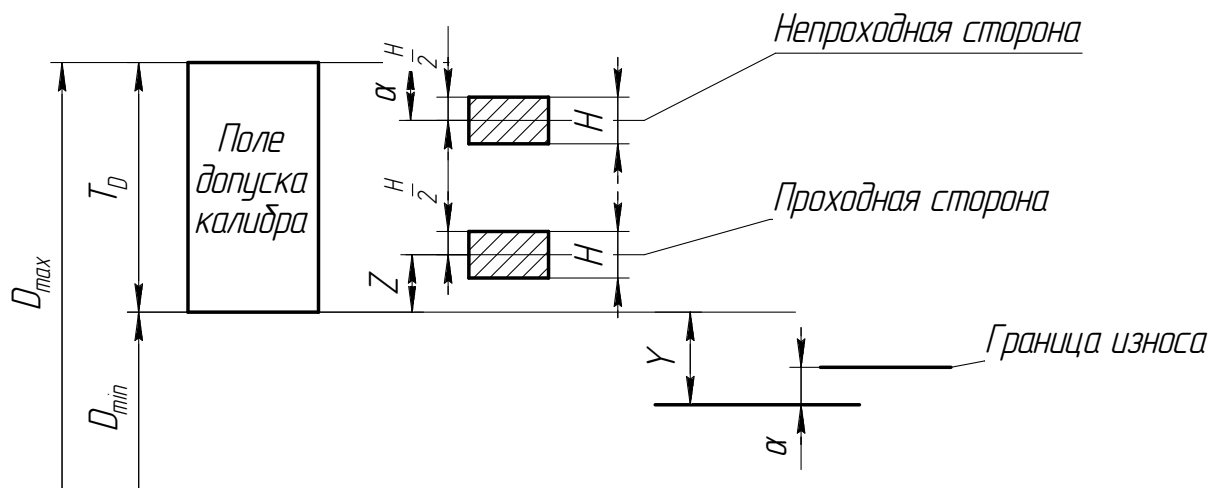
Схема расположения полей допусков калибров для контроля отверстий
